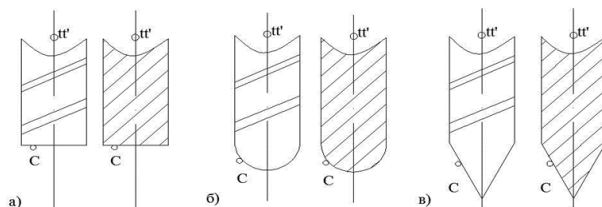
Схема торкання фрези з контрольованою геометрією: а) кінцевої циліндричної; б) сфероциліндричної; в) конічних фрезами
